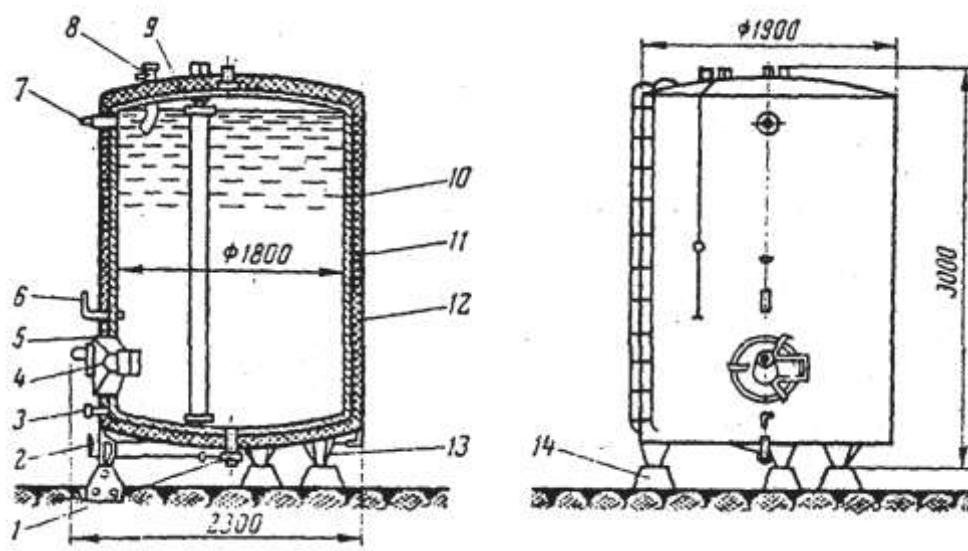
Резервуар РМВЦ-6 для зберігання молока
